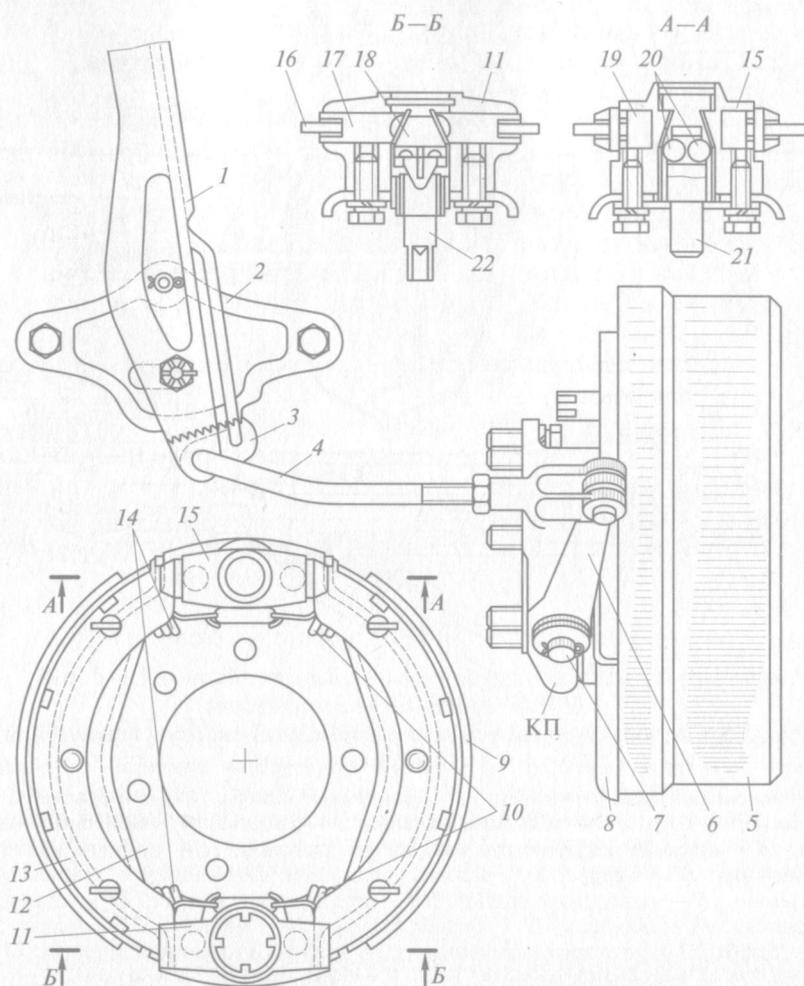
Стояночный тормоз автомобиля ГАЗ-53А:
